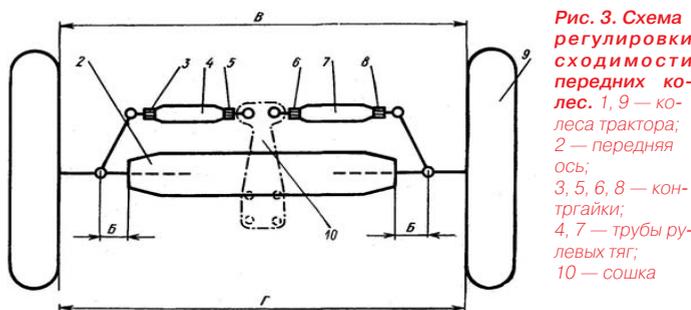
Схема регулировки сходимости передних колес. 1, 9 — колеса трактора; 2 — передняя ось; 3, 5, 6, 8 — контргайки; 4, 7 — трубы рулевых тяг; 10 — сошка
